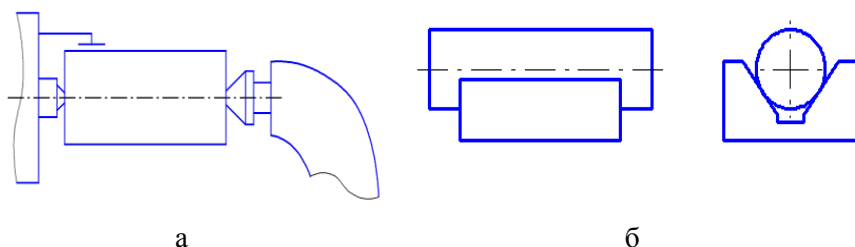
Закрепление валов: а) закрепление в центрах; б) закрепление в призме
